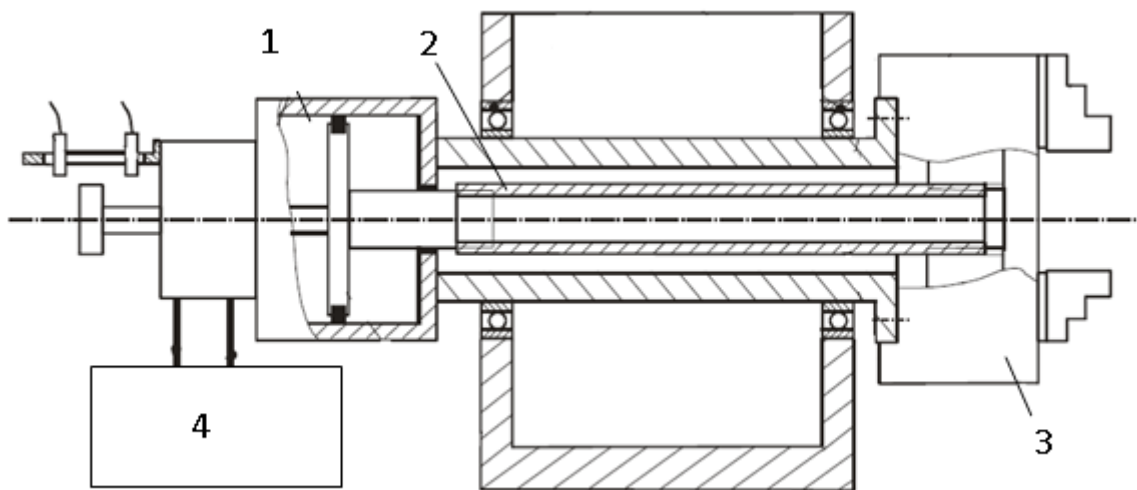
Типова схема автоматичного затискного механізму токарного верстата
